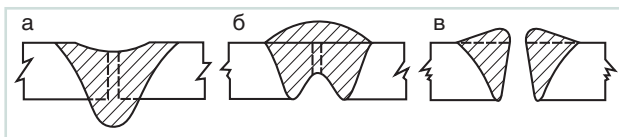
Форма стыкового шва при односторонней сварке на флюсовой подушке: а — при слабом поджатии флюса; б — при сильном поджатии флюса; в — при большом зазоре в стыке
